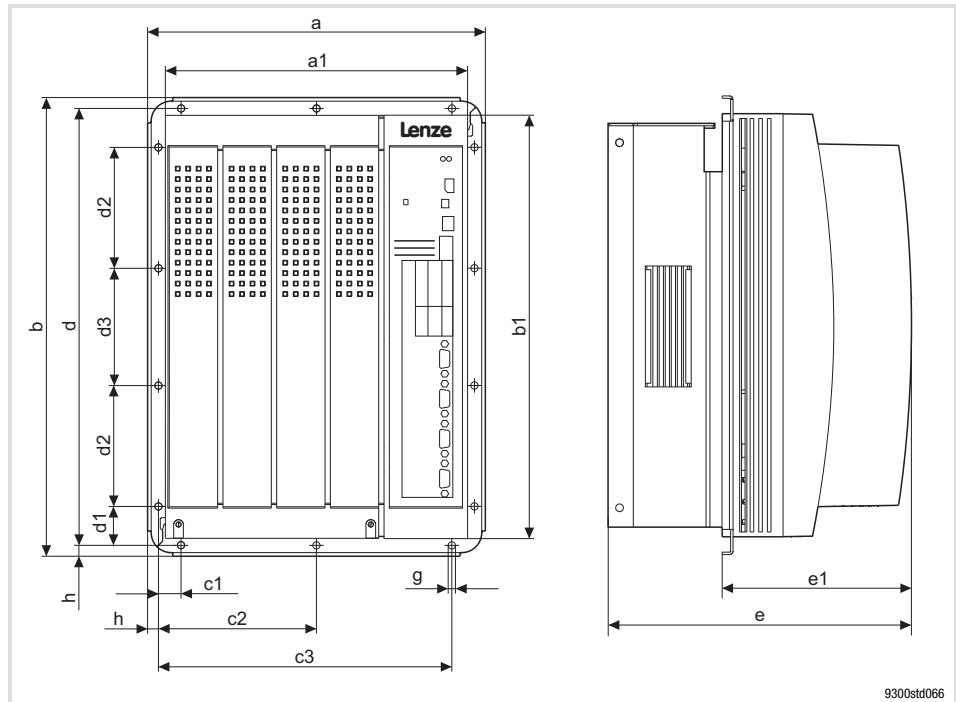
Abmessungen Montage thermisch separiert 15 ... 30 kW
